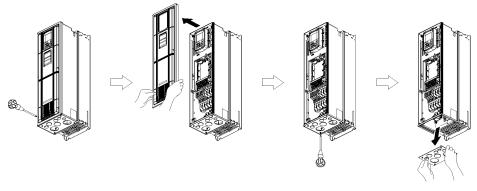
Retrait du couvercle avant et de la plaque de câblage (FRN37AQ1M-4□)
